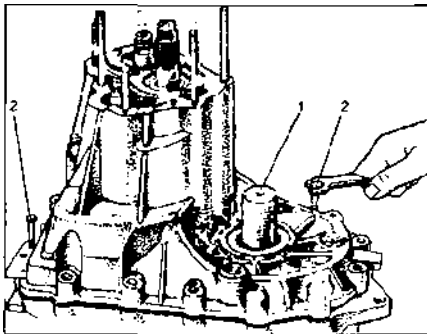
Завертывание упорных болтов в картер коробки и установка оправки в шестерню полуоси:
